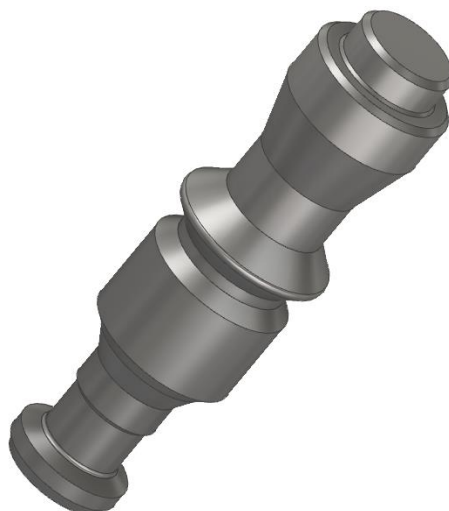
3D-модель заготовки байонетного гвинта
